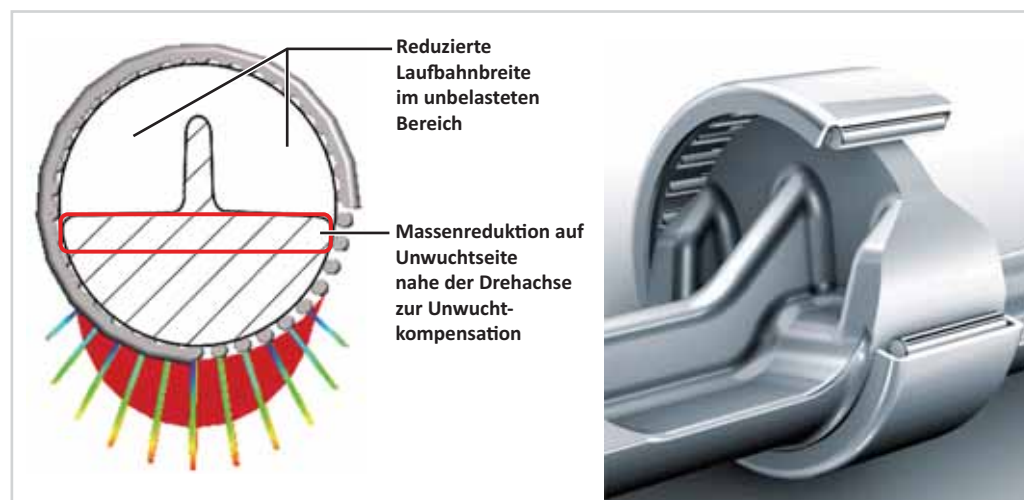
Optimierte Gestaltung einer Ausgleichswellenwälzlagerung
